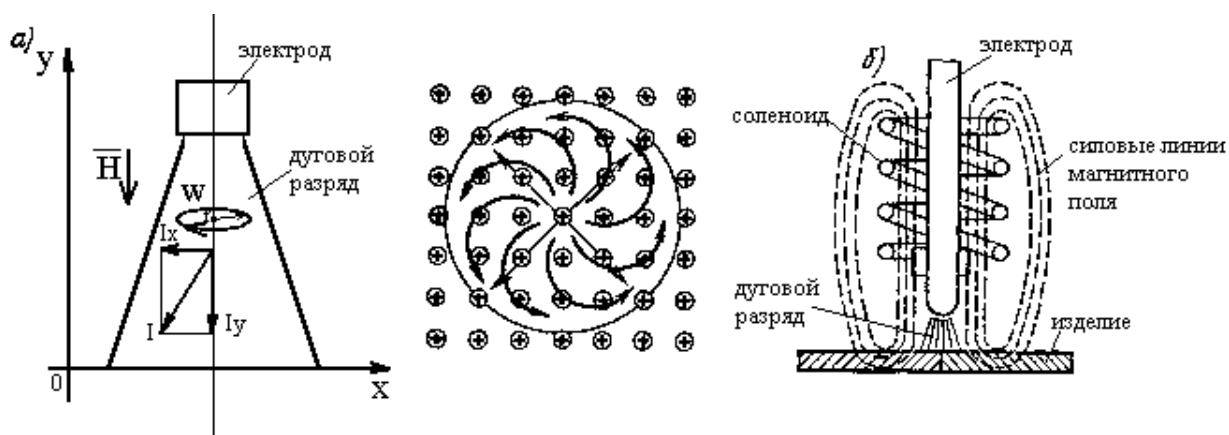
Действие продольного магнитного поля на сварочную дугу (а) и схема направляющего соленоида (б)
